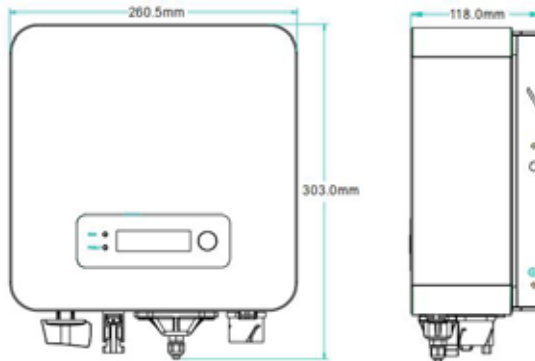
Dimensions vue de face et vue de gauche SOFAR 3300TL-G3
